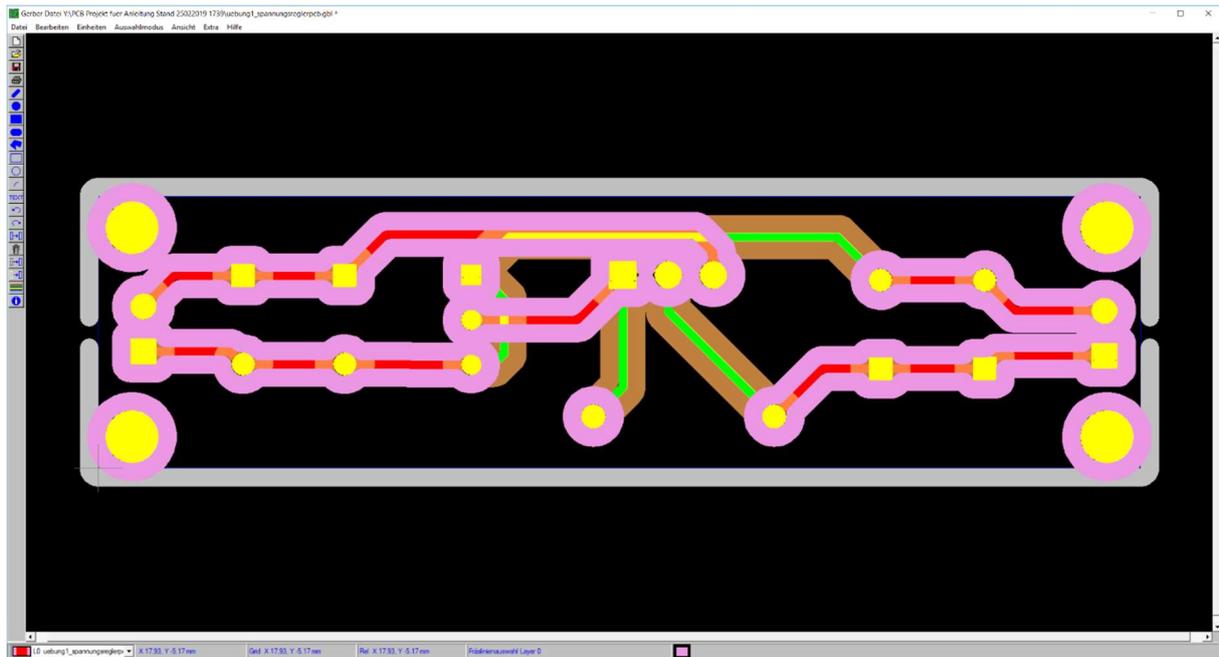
Erzeugte Fräslinien Bottom Layer
